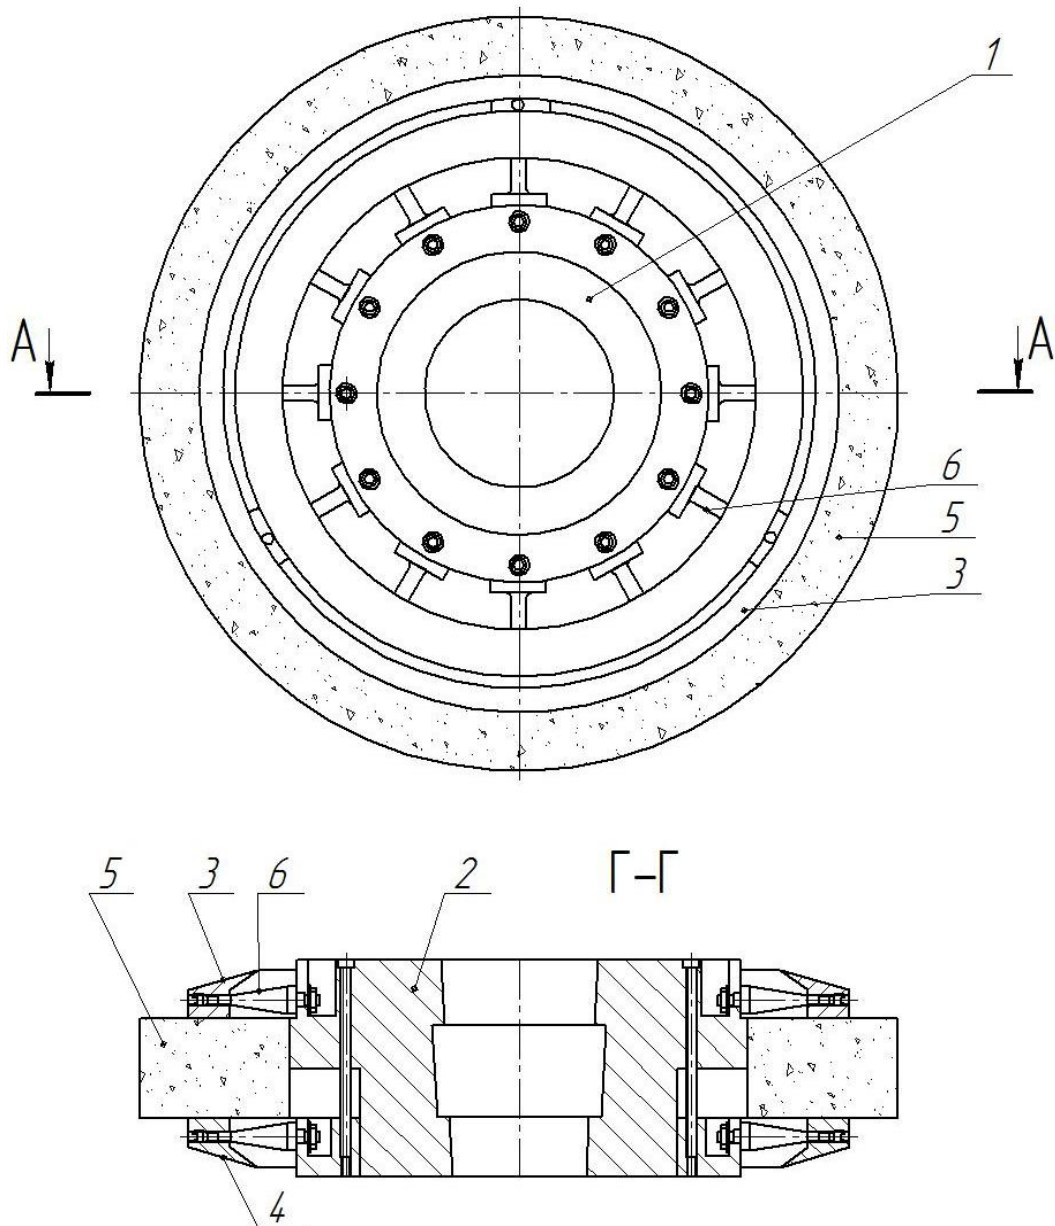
Эскиз круга с торсионным корпусом
